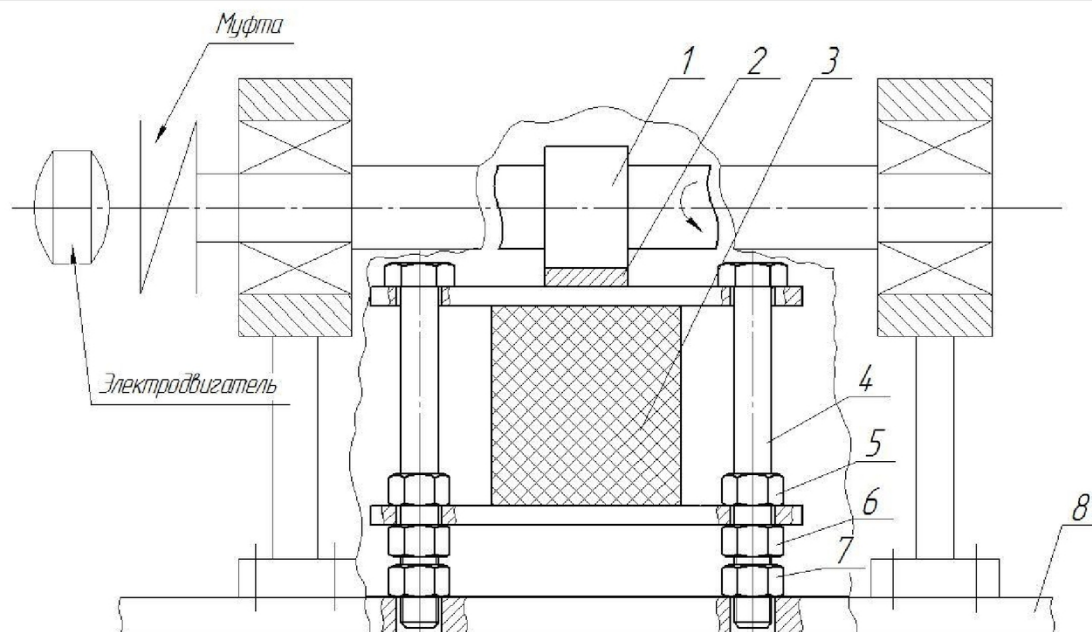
Схема нагружающего устройства: 1 - эксцентрик; 2 - пята; 3 - амортизатор; 4 - направляющий винт; 5 - контр-гайка; 6 - подъемная гайка; 7 - фиксирующая гайка; 8 - основание.
